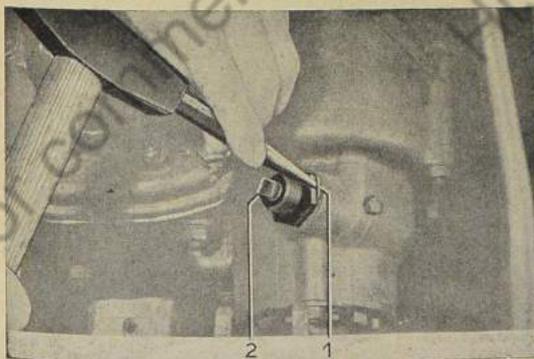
Anschlußstück für Geschwindigkeitsmesser herausschrauben
